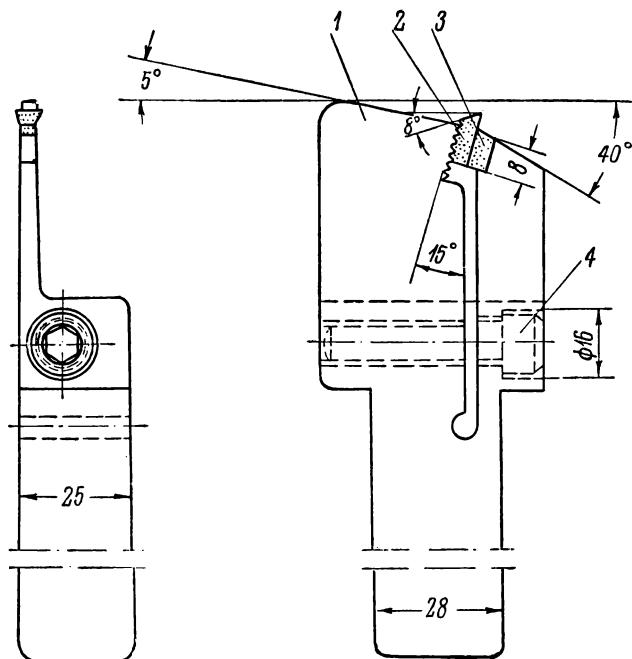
Отрезной резец с креплением режущей пластинки силами резания конструкции Н. Е. Сотникова.
